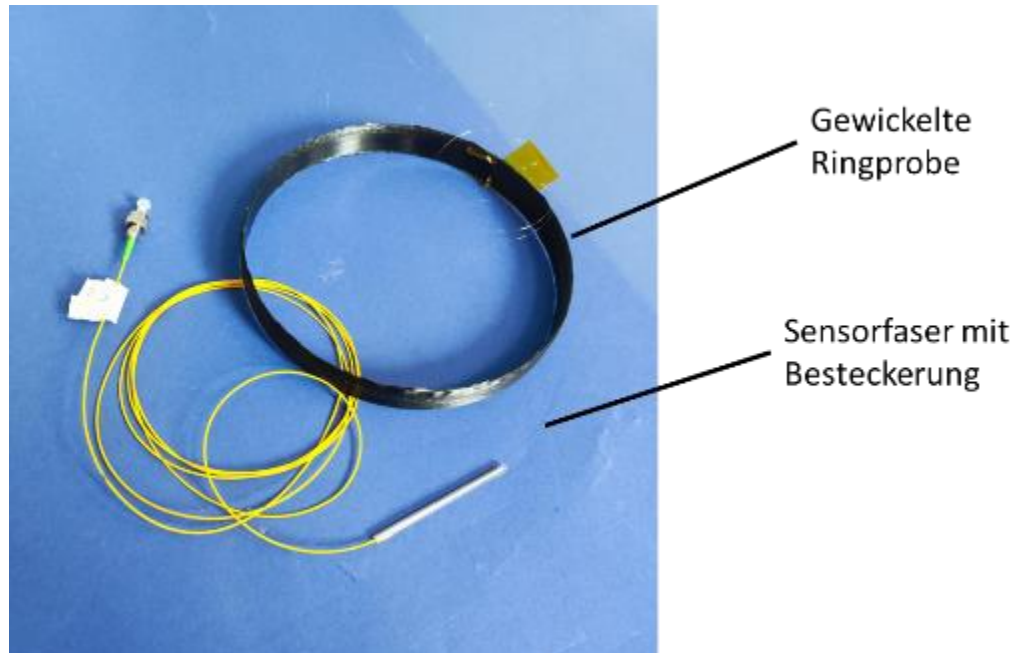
Gewickelte Ringprobe mit einseitiger Besteckung.
